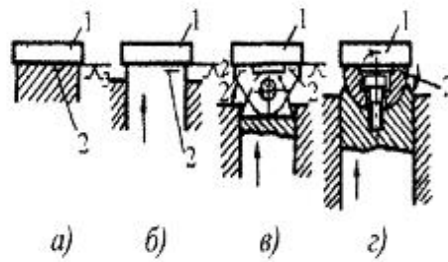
Закріплення призматичної заготовки 1 направленими затисками
